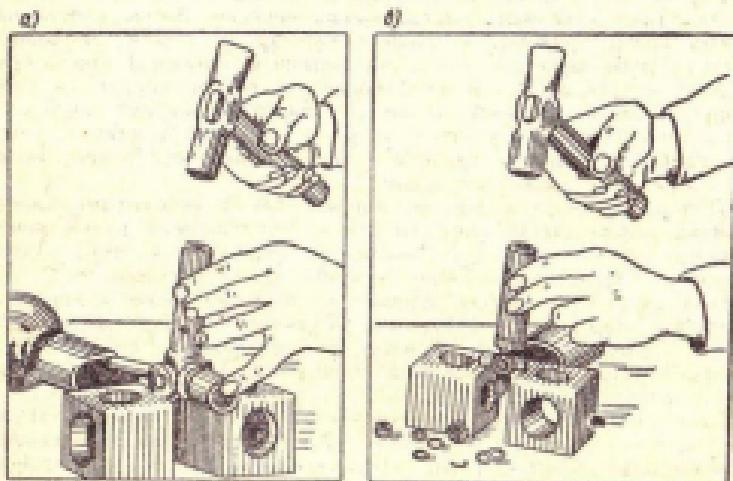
Присыны разборки и сборки карданного шарнира:
